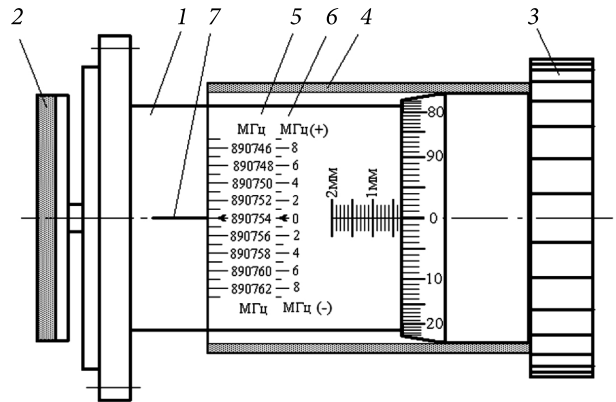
Схема мікрометричного механізму переміщення дзеркала зі шкалами частотного налаштування та різниці частот: 1 — корпус механізму переміщення дзеркала; 2 — дзеркало резонатора; 3 — рукоятка обертання з мікрометричною шкалою; 4 — прозора насадка зі шкалою частотного налаштування 5 та шкалою відстройки від центральної частоти 6; 7 — нерухомий курсор
